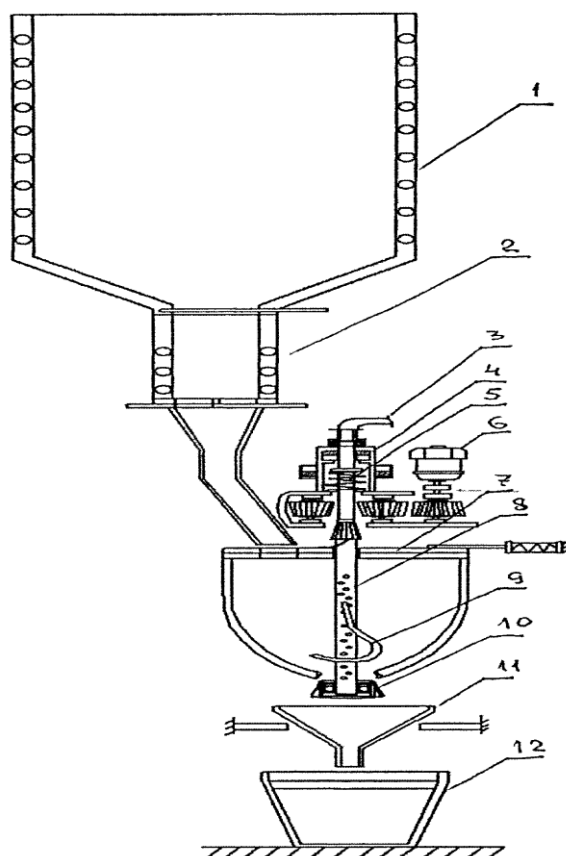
Устройство для измельчения при приготовлении «смузи» [6]
